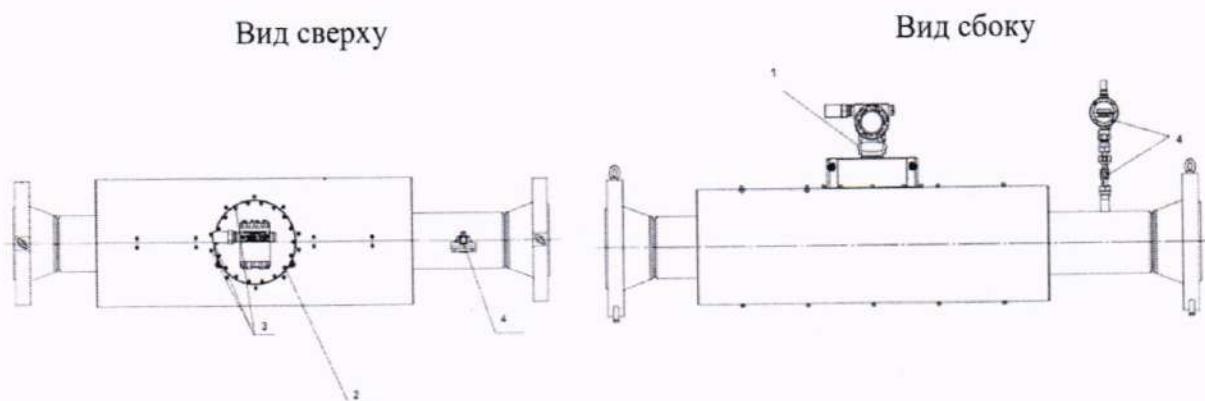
Корпус круглого сечения с защитным кожухом
